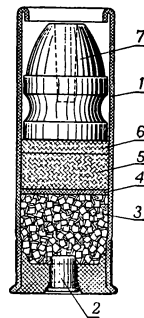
Патрон, снаряженный цилиндрико-оживальной пулей для стрельбы из нарезного чока — сверловка «парадокс»:
